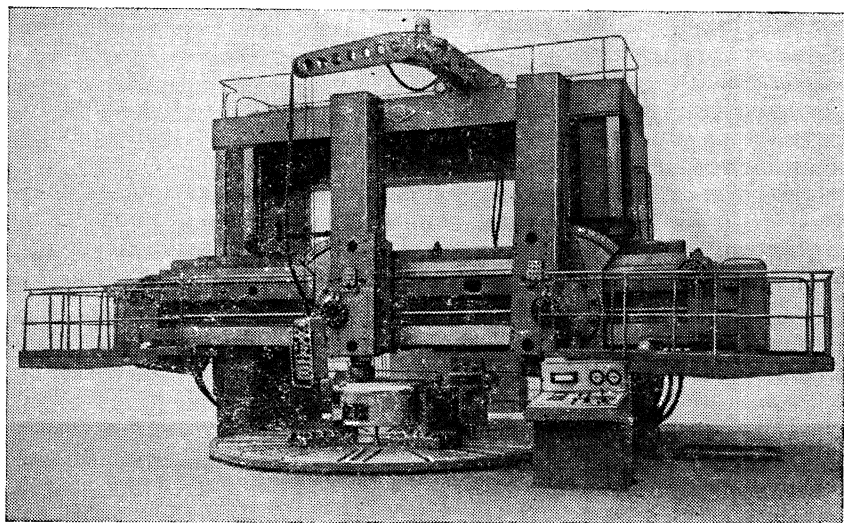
Токарно-карусельный двухстоечный универсальный станок мод. 1550
